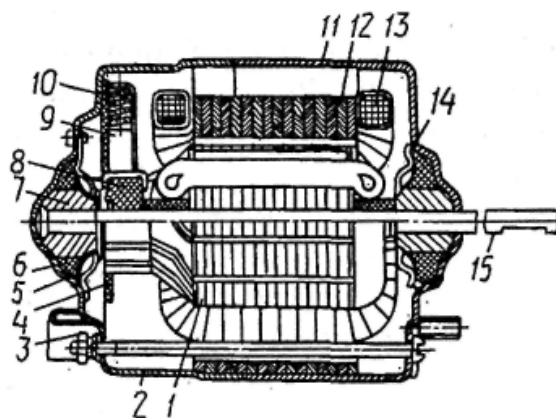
Електродвигун з електромагнітним збудженням М3201 1 -якір; 2 - кришка; 3 – стяжний гвинт; 4 - траверса; 5, 14- пластинчасті пружини; 6 - набивка; 7 - підшипники; 8 - колектор; 9 - щітка; 10 - щіткотримач ; 11 - корпус; 12 - пакет статора; 13-обмотка збудження; 15-вихідний вал
